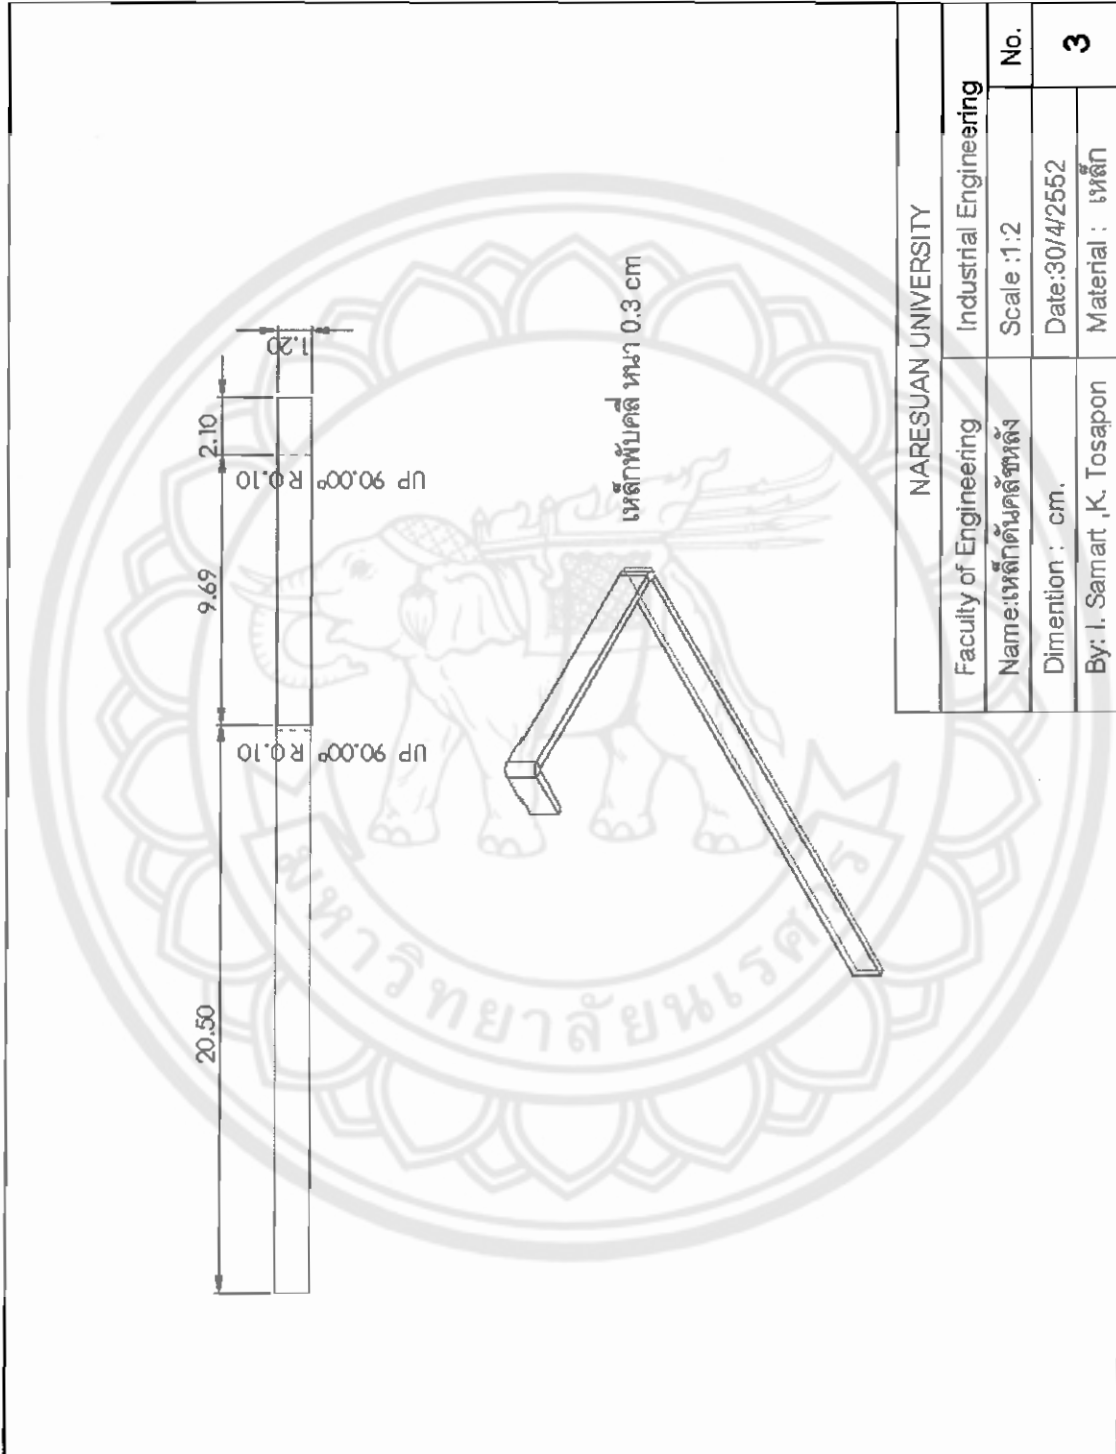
แสดง Assembly Drawing ตัวค้ำหลัง
